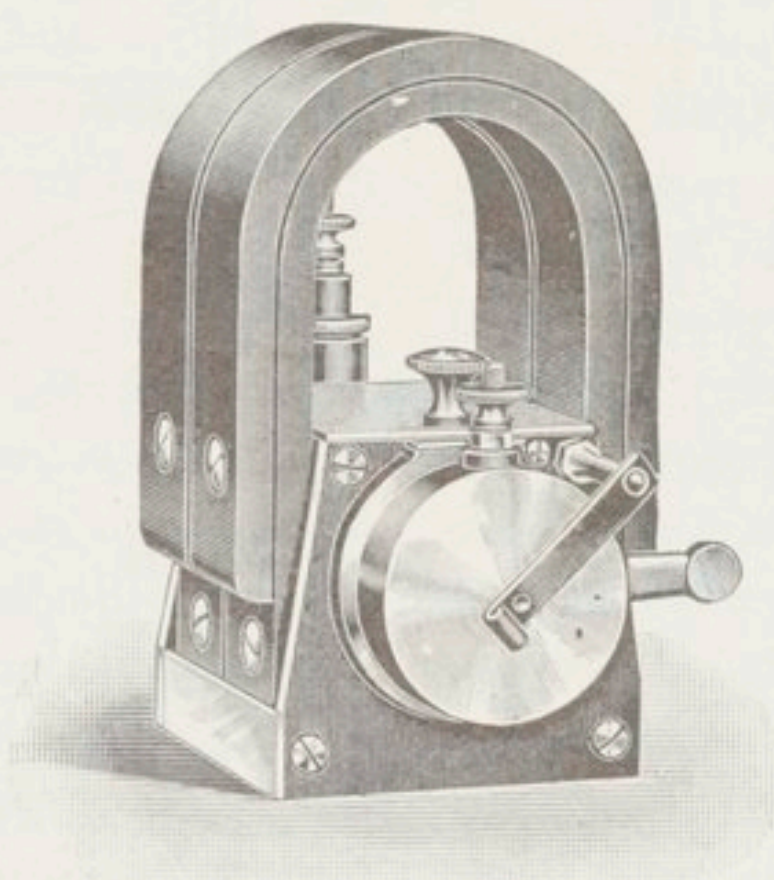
Magnéto à bougies Bosch pour moteur à un cylindre. Vue d'ensemble.
